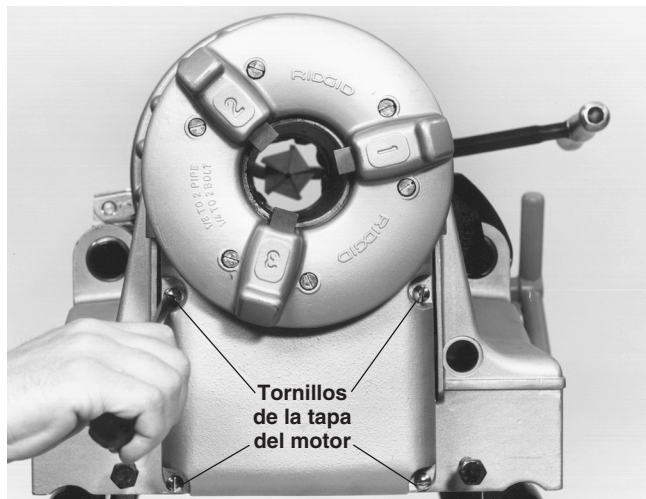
Soltar y extraer los tornillos de la tapa del motor
